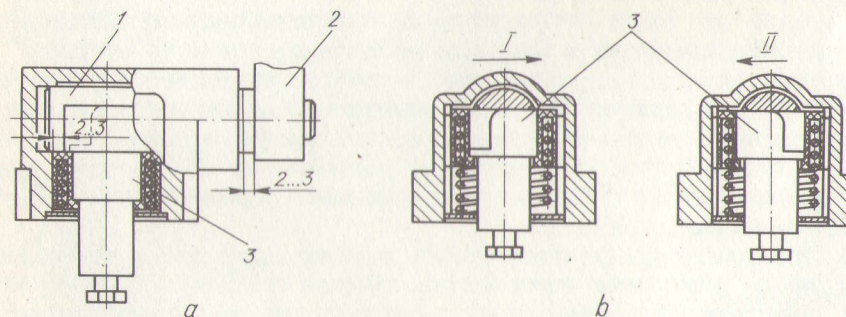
Привод селективный: 1 — вал; 2 — рычаг; 3 — толкатель; I — рабочий ход вправо; II — рабочий ход влево
